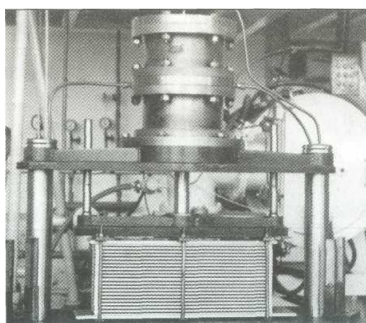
Прес для складання пакета деталей ПРЕ
